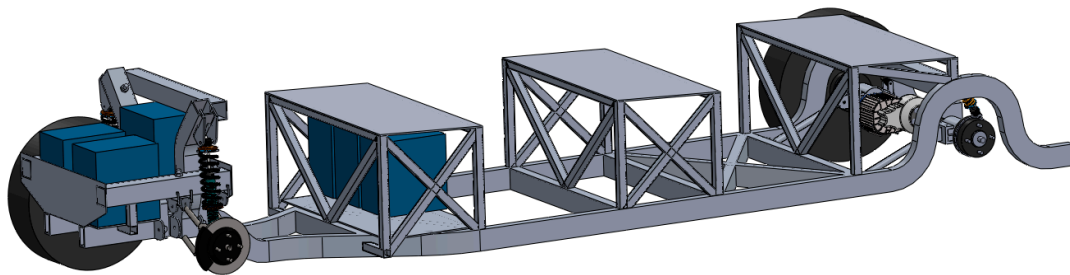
Desenho inicial do conjunto (perspetiva de frente)
